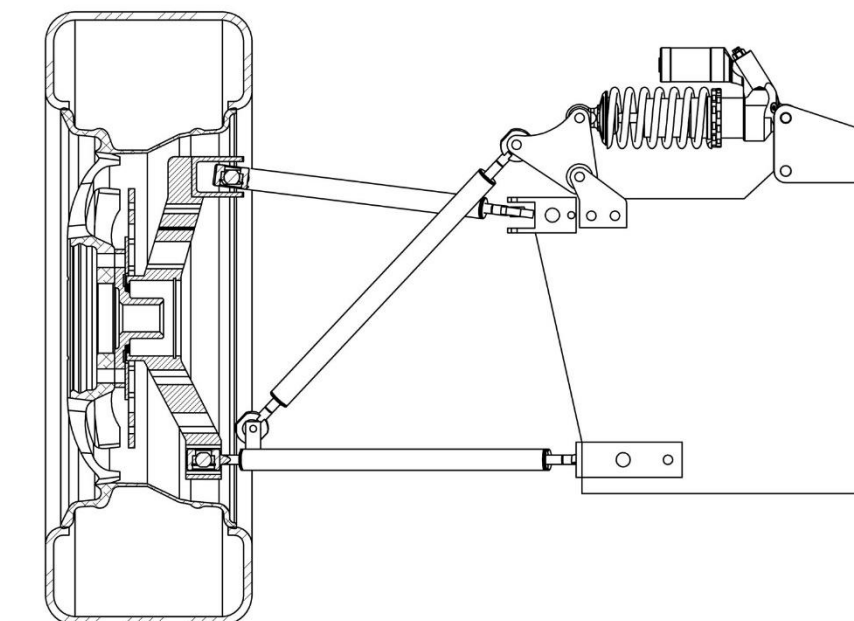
Схема конструкции подвески с толкающей тягой (Push rod)
